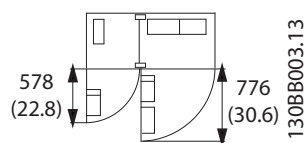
Пространство перед корпусом типа IP21/IP54, типоразмер F1.
